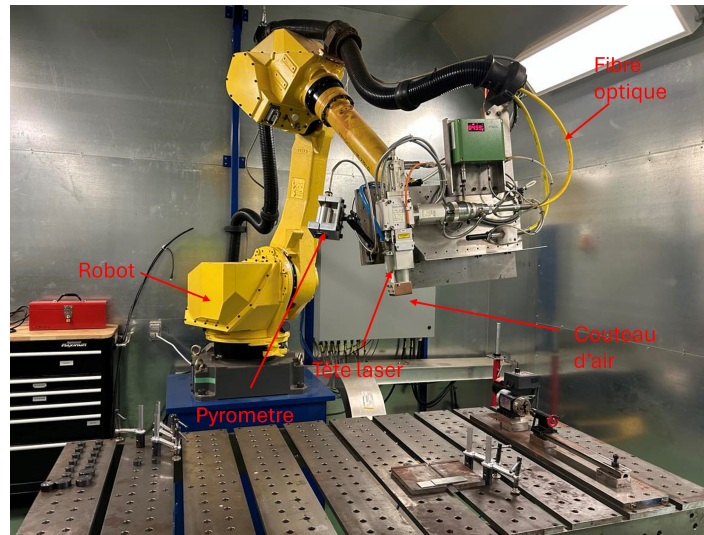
Robot 6 axes utilisé pour les soudures
